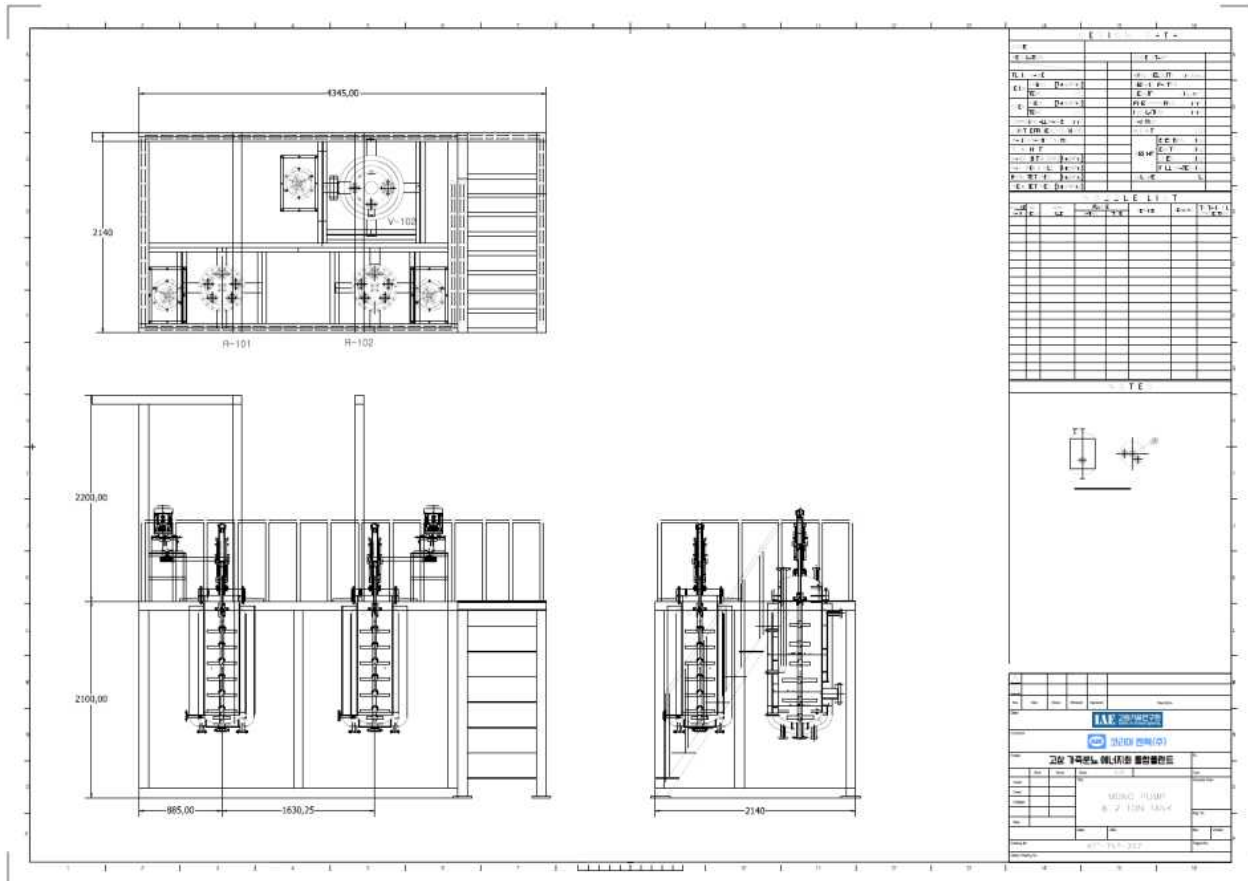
Pilot plant급 수열탄화 시스템 구조물 및 설비배치도 설계도면
